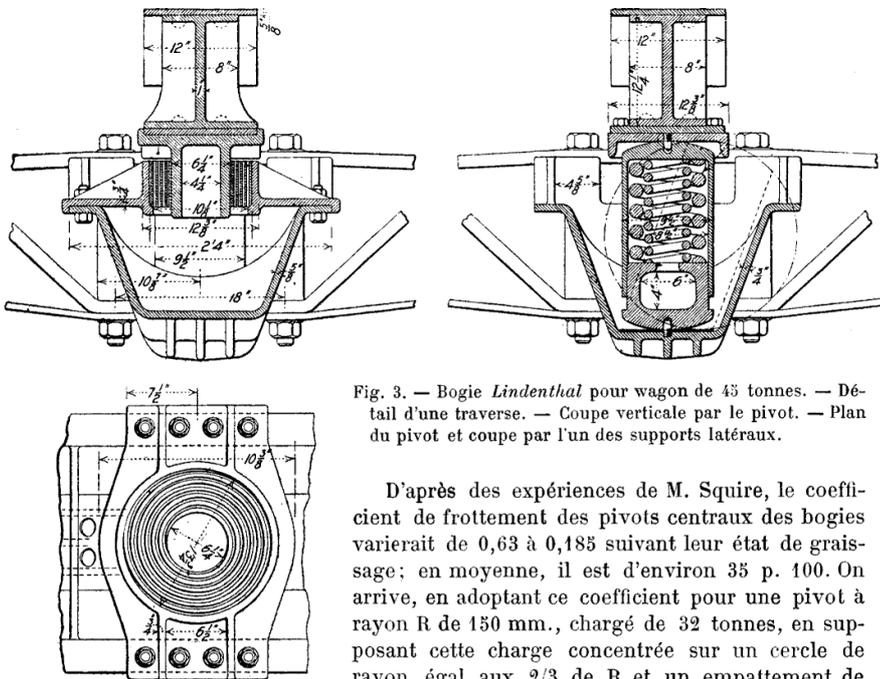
Bogie Lindenthal pour wagon de 43 tonnes. — Détail d'une traverse. — Coupe verticale par le pivot. — Plan du pivot et coupe par l'un des supports latéraux.
